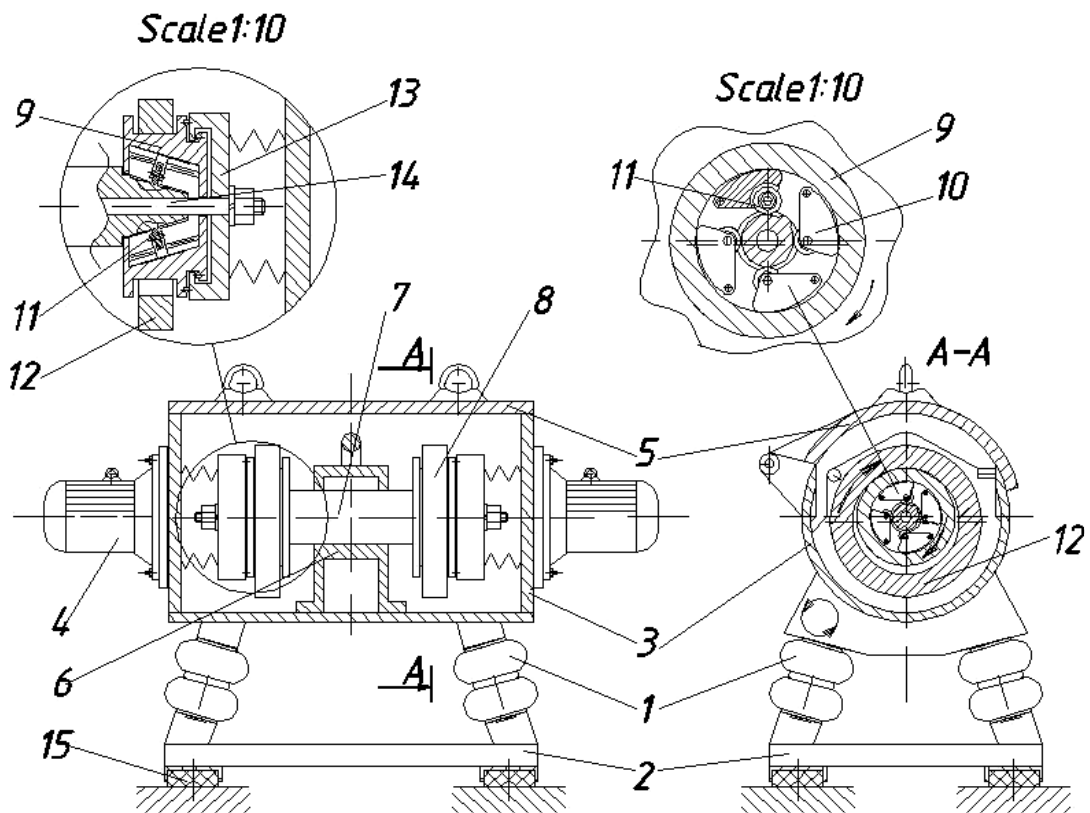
Конструкція машини для вібраційно-відцентрового зміцнення різьбових поверхонь [22]
